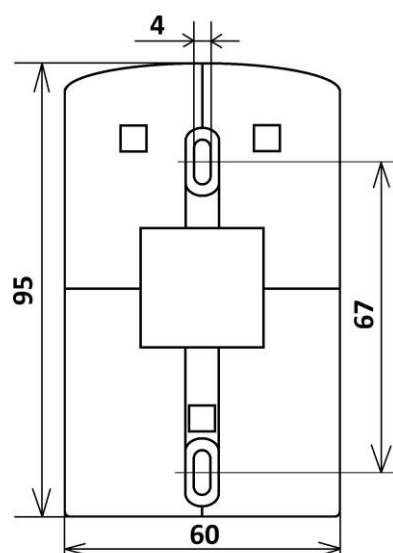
Габаритные и установочные размеры крепежной пластины
